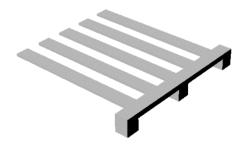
托盘可移动部分 Fig.3 Movable part arrangement of the pallet
